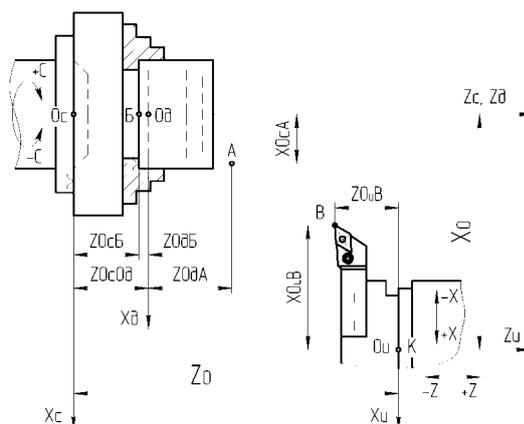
связь систем координат токарного станка с ЧПУ
